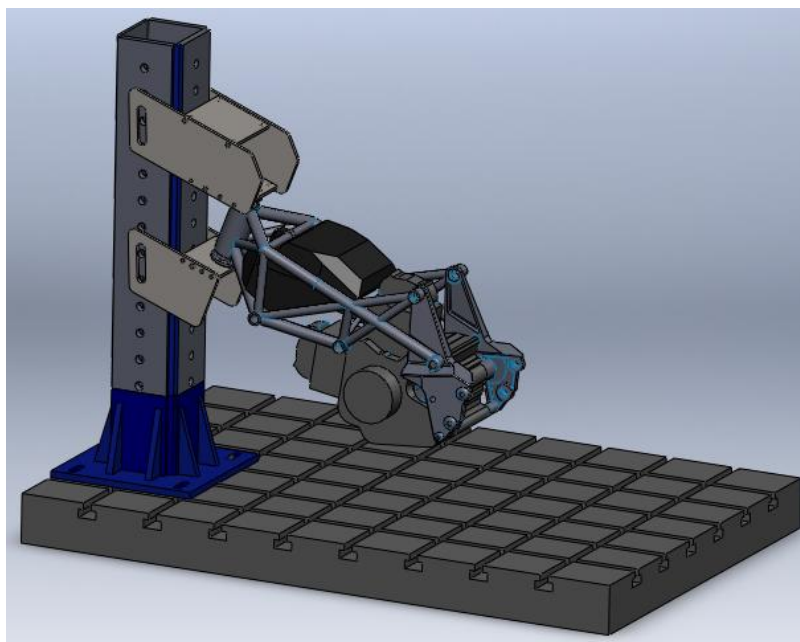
Disegno 3D del banco prova: assieme fissaggio e telaio
